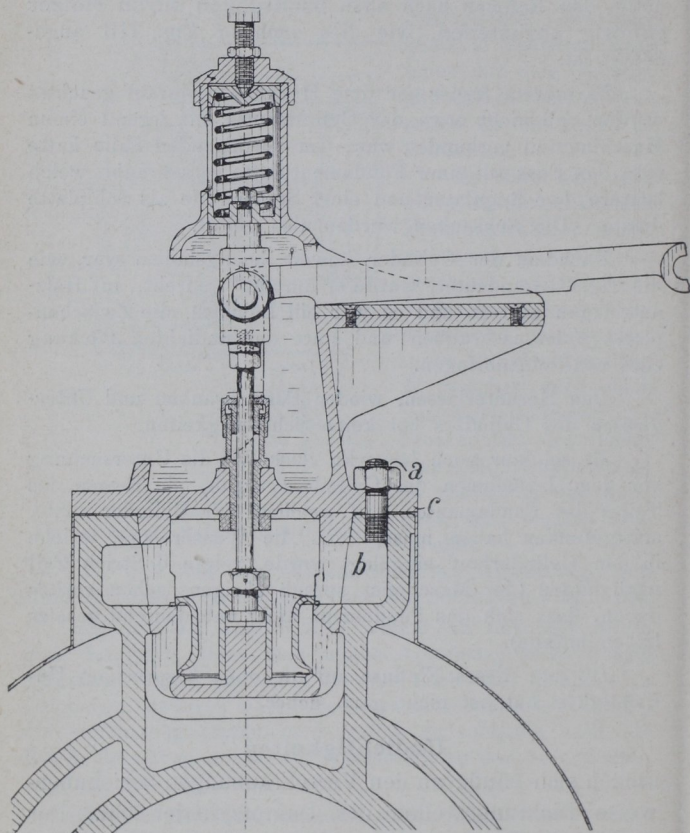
Einlassventil mit undichten Schrauben der Ventildeckel.
